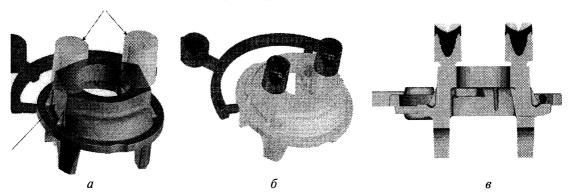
Результаты моделирования: a — общий вид отливки с литниковой системой; δ — отливка с литниковой системой после охлаждения; ϵ — разрез охлажденной отливки по месту образования раковин
